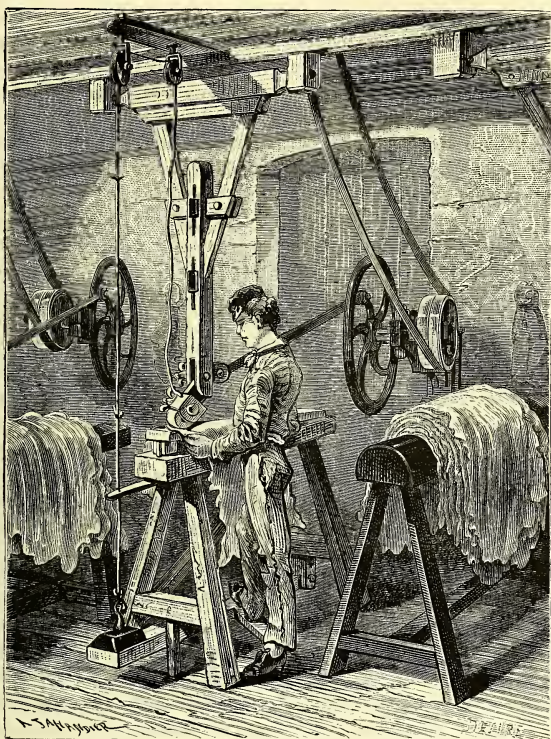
Ouvrier lissant le maroquin avec la machine à lisser.
